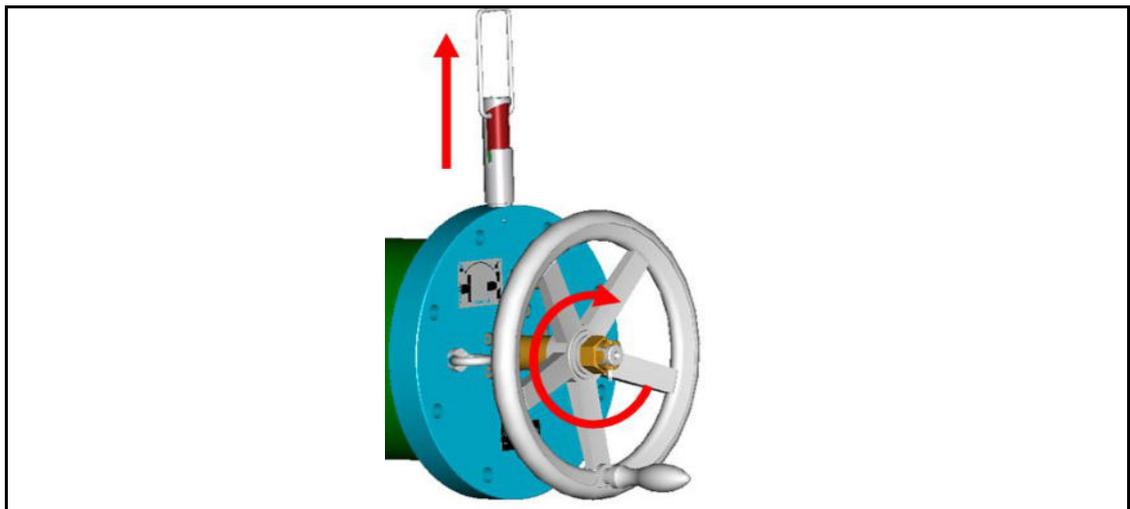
Rotorarretierung entriegeln (Abb. ähnlich)
